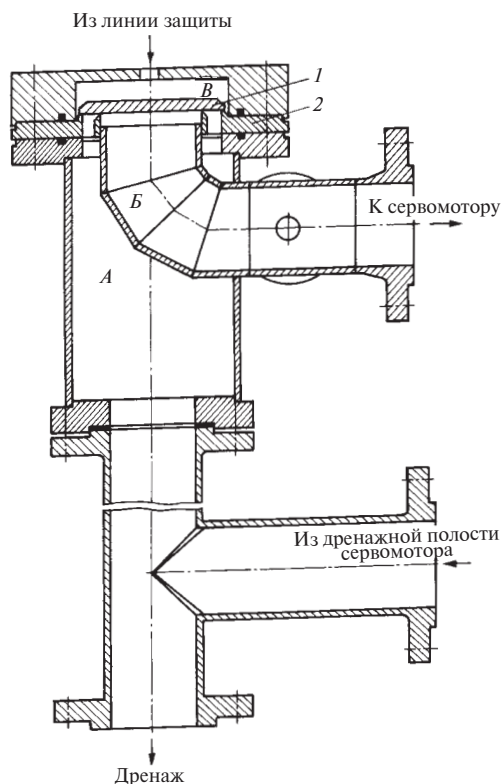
Выключатель сервомотора стопорного клапана:
